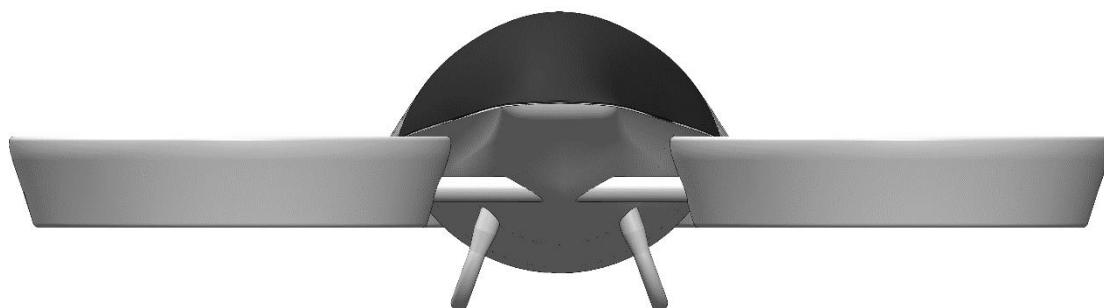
Vista trasera alzado. Fuente: elaboración propia
